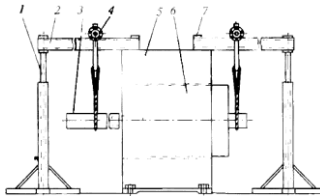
Схема ввода ротора в статор при отсутствии грузоподъемных механизмов: 1 — стойка; 2 — балка; 3 — удлинитель; 4 — грузовой ролик; 5 — статор; 6 — ротор; 7 — накладка
